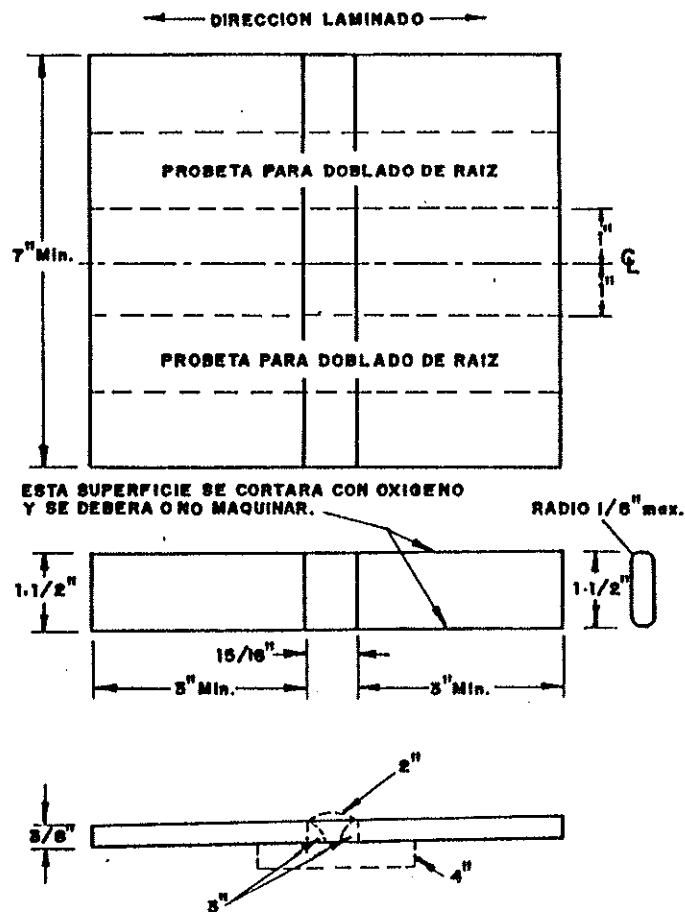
Soldadura de Filete para ensayo de doblado de placa.
